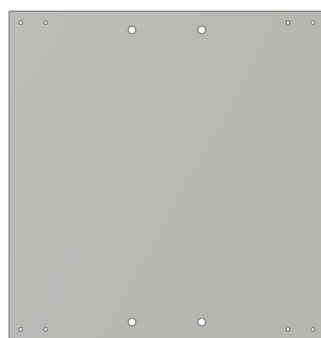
Vista isométrica da placa de ACM que será utilizada como base após o corte.
